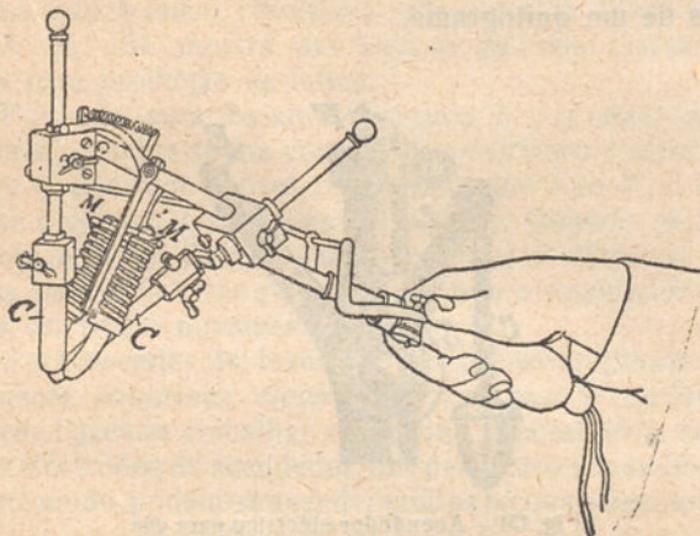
Aparelho Zereener de soldadura pelo arco
